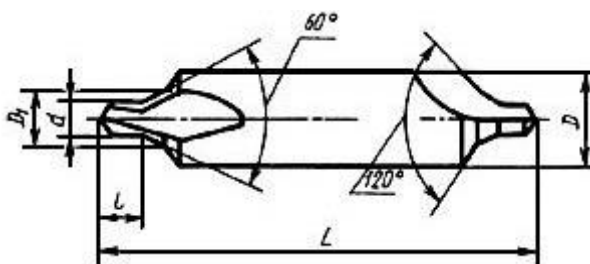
Центровочное сверло 2317-0108ГОСТ 14952-75
